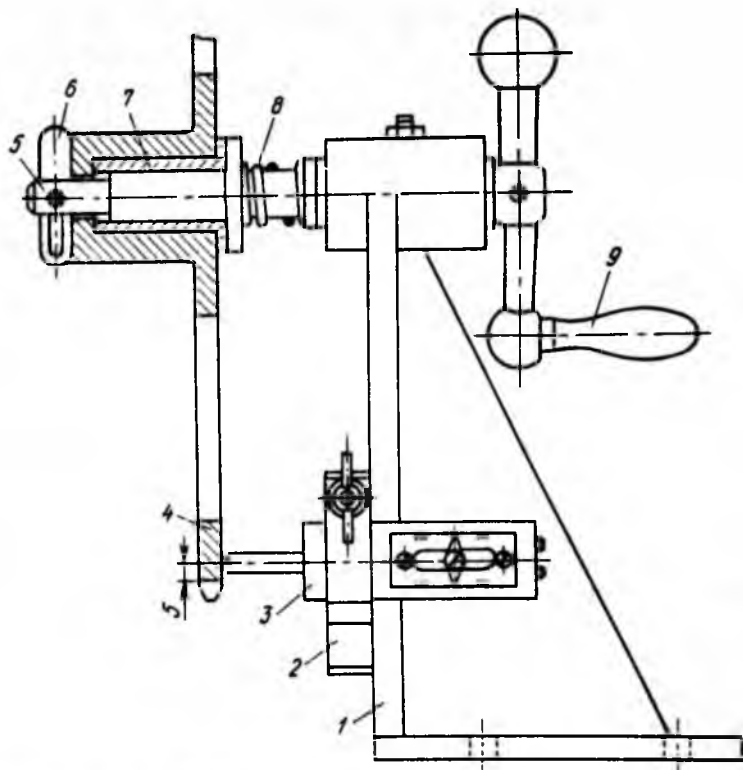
Приспособление КИ-2195 для контроля торцевого биения звездочек:
